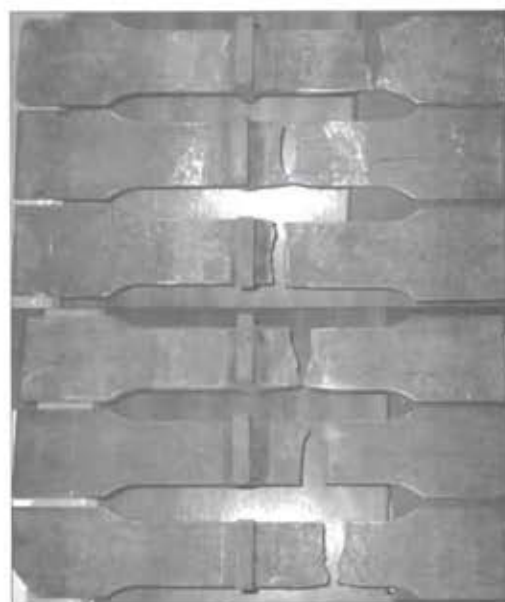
Общий вид упрочненных образцов таврового сварного соединения стали 10XCHD, разрушенных после испытаний на усталость в коррозионной среде
